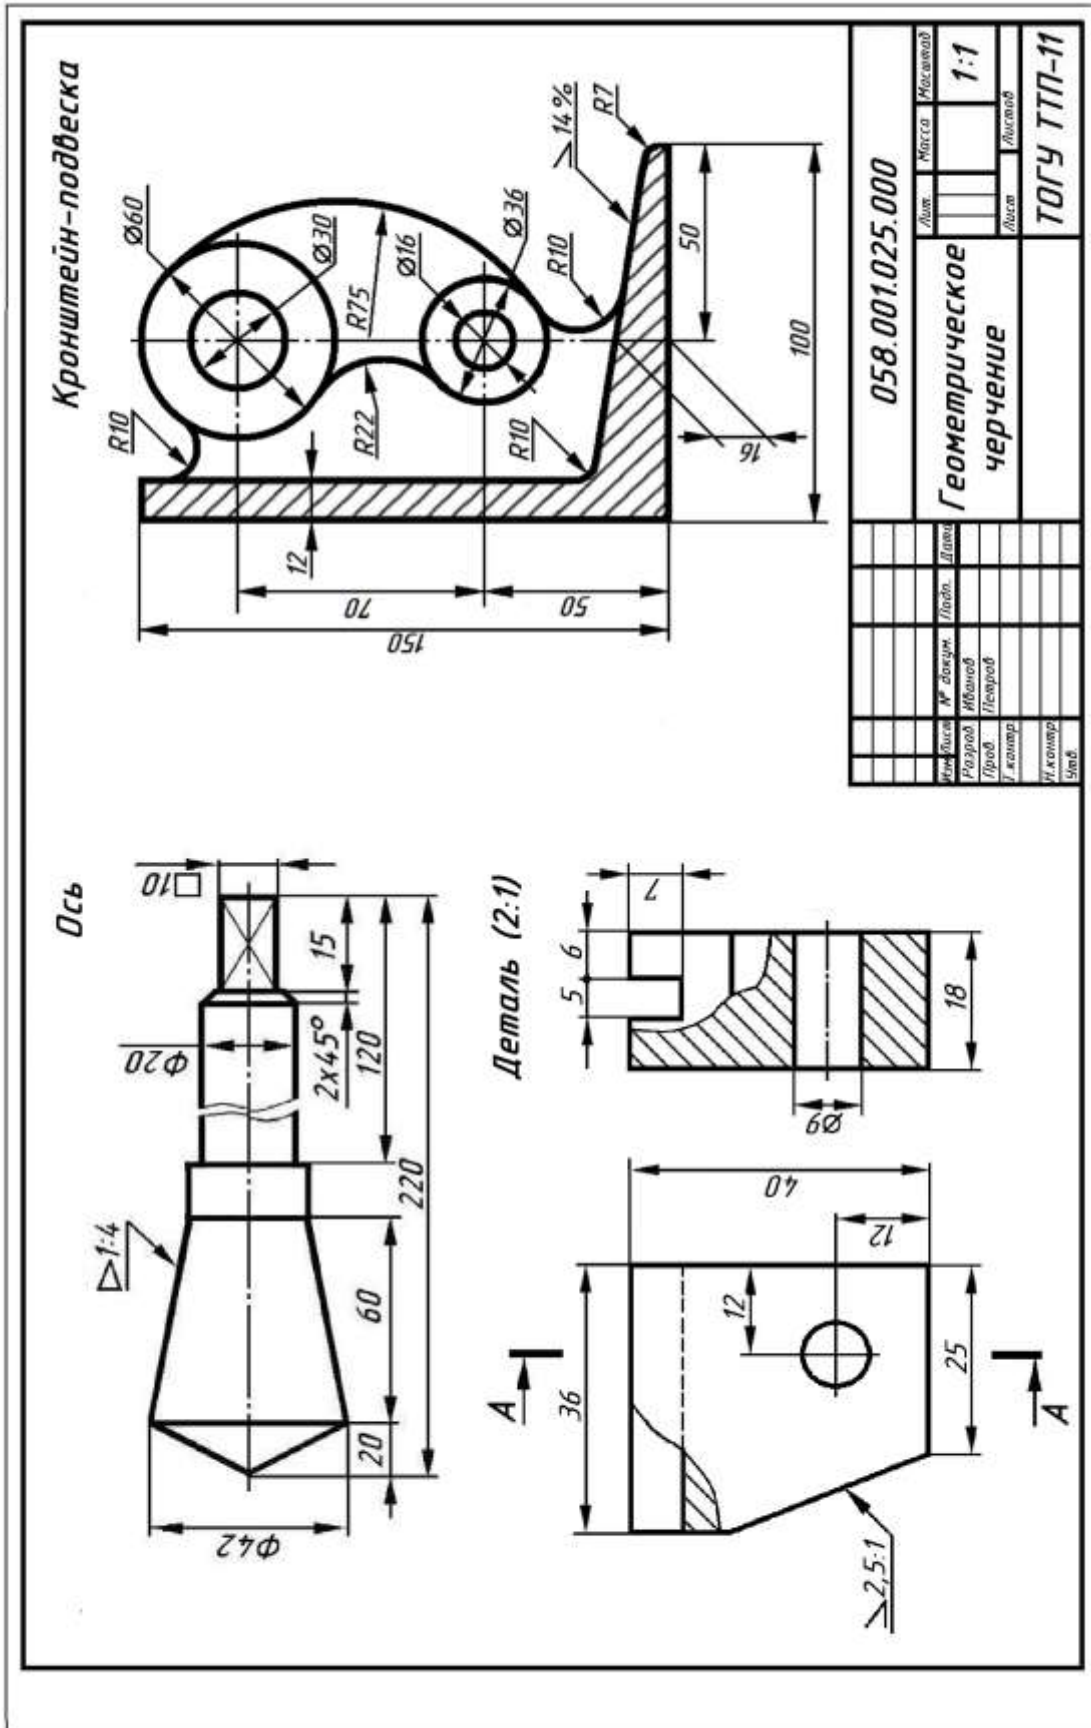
Размеры и расположение стрелок и разомкнутой линии
